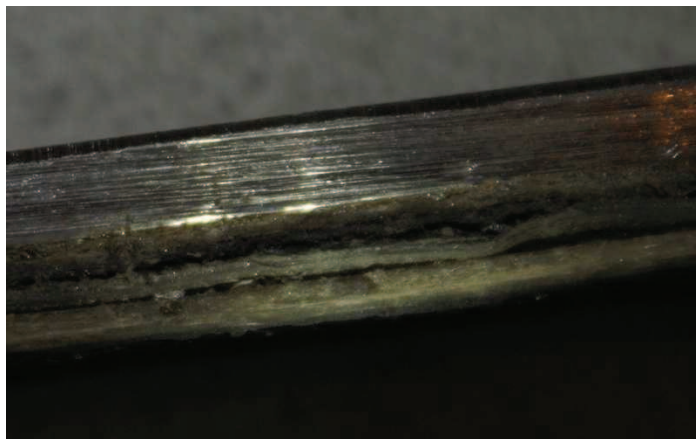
Przykład ścianki z laminatu z przestrzenią do monitorowania wycieków
